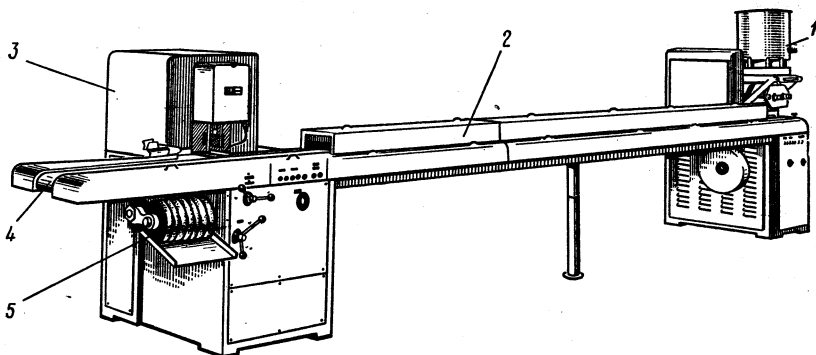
Универсальный формующий агрегат LP-100 для формования конфет вы-прессовыванием и обкаткой:
